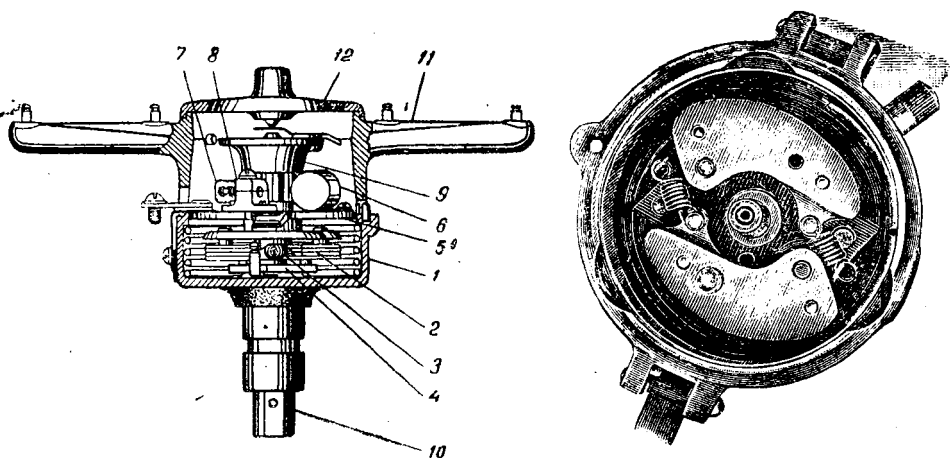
Разрез прерывателя-распределителя и вид регулятора опережения зажигания:
